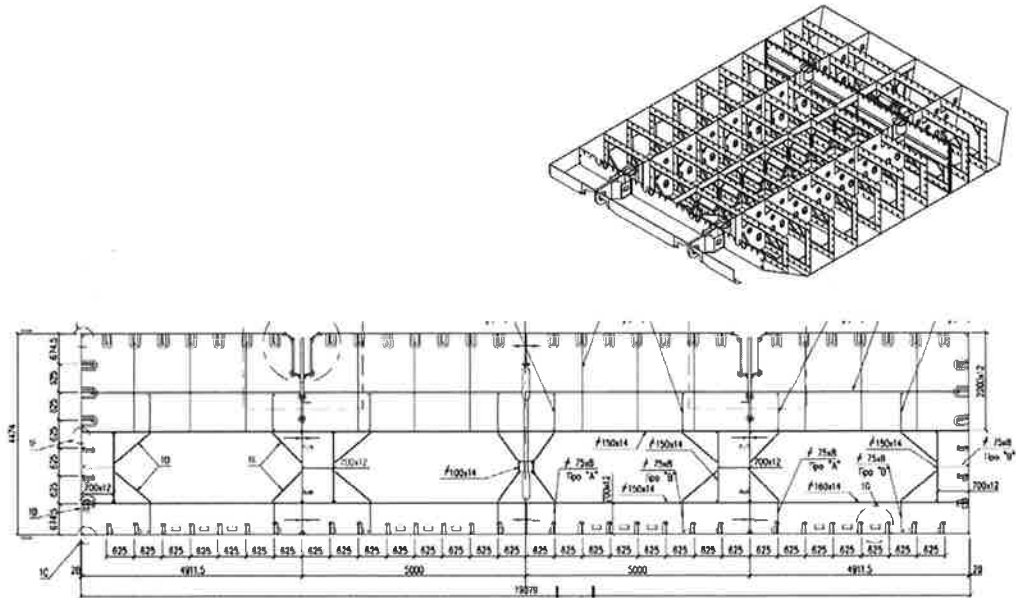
TELAIO TRASVERSALE 9 CON PARETE STAGNA
